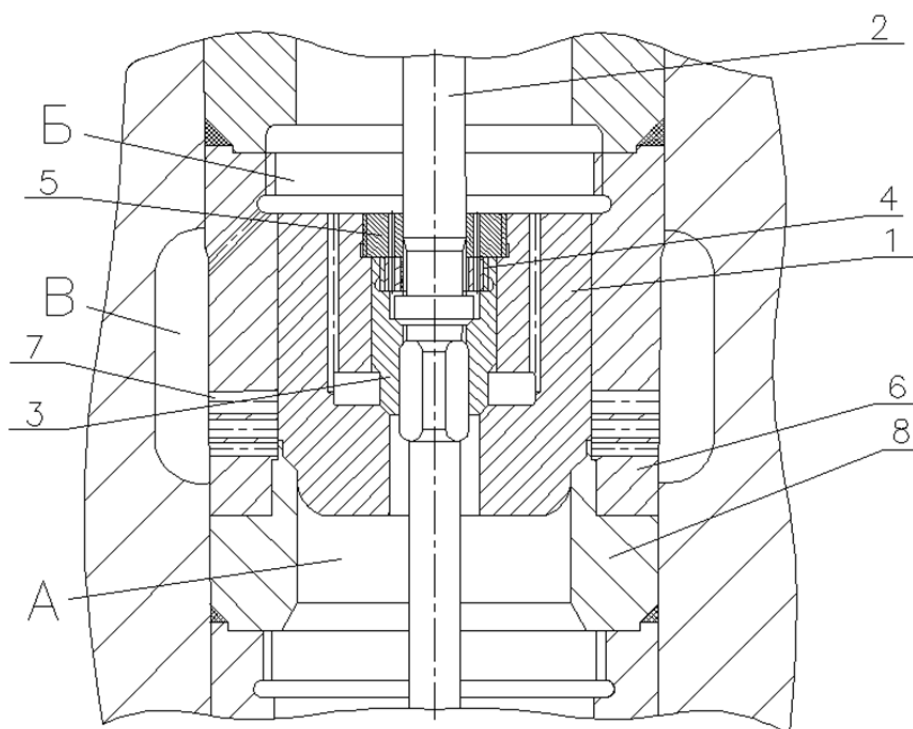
Типовая конструкция клапанов управления рабочими и возвратными цилиндрами гидравлического пресса с разгрузкой:
